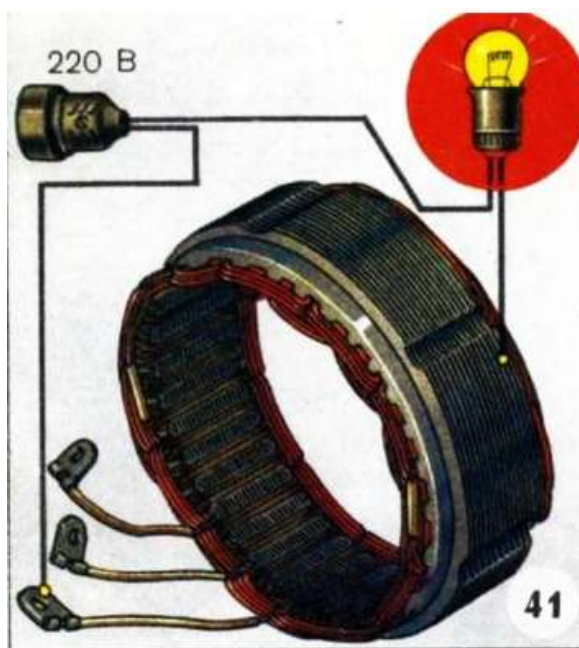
Проверка обмотки статора на замыкание с корпусом
